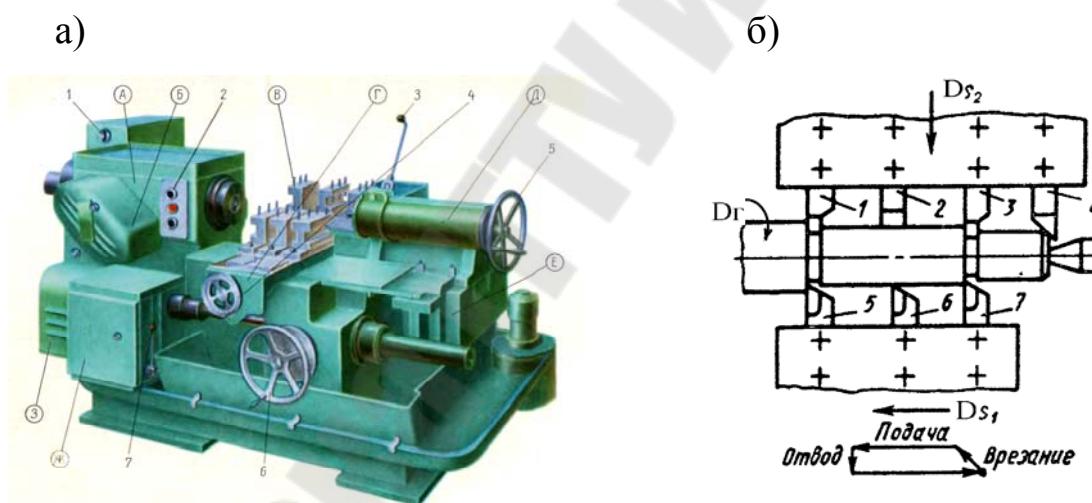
Общий вид многорезцового станка (а) и схема обработки (б)
